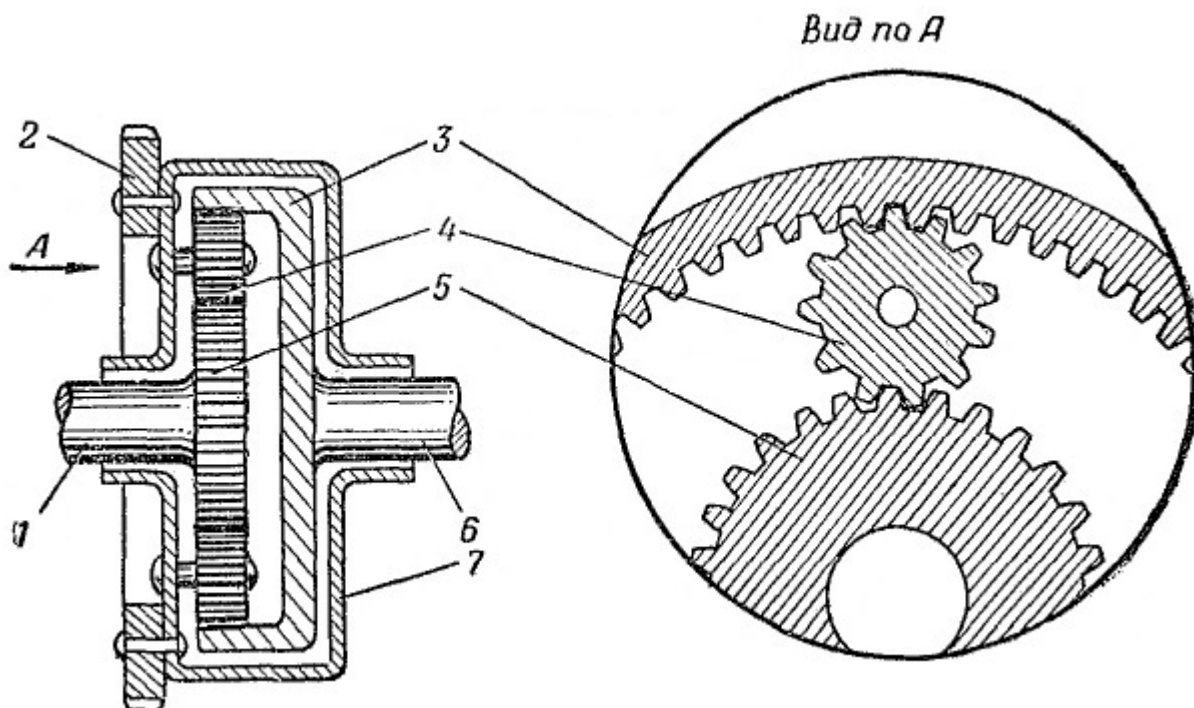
Схема межосевого несимметричного планетарного дифференциала: 1 — вал привода переднего ведущего моста; 2 — ведомая шестерня дифференциала; 3 — коронная шестерня; 4 — сателлит; 5 — солнечная шестерня; 6 — вал привода среднего и заднего ведущих мостов; 7 — коробка дифференциала
